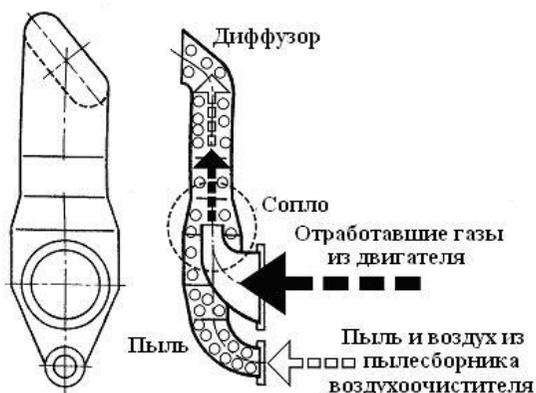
Схема эжектора системы автоматического удаления пыли из пылесборника воздухоочистителя двигателя
